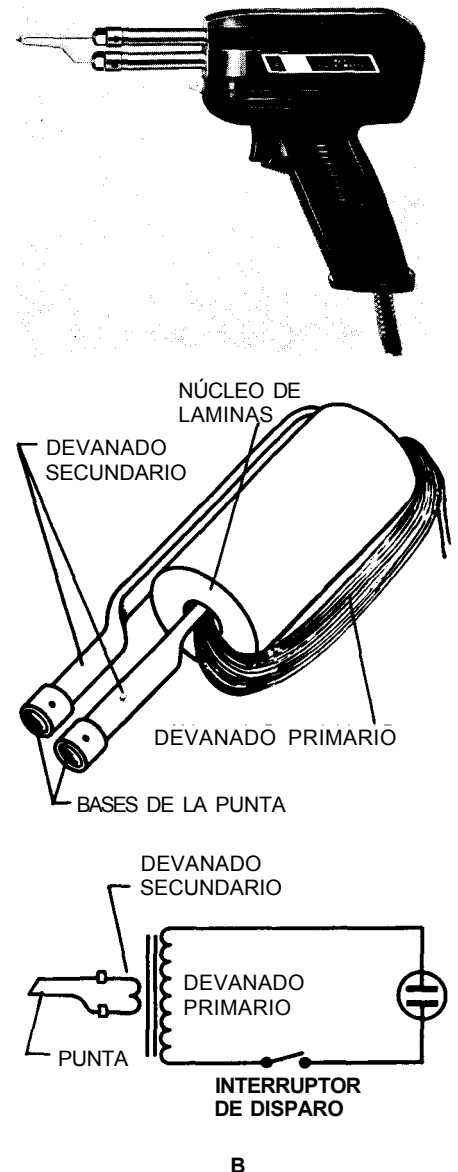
(A) pistola típica para soldar; (B) detalles de la estructura y diagrama esquemático de una pistola para soldar común (Cortesía de Weller Electric Corporation).
